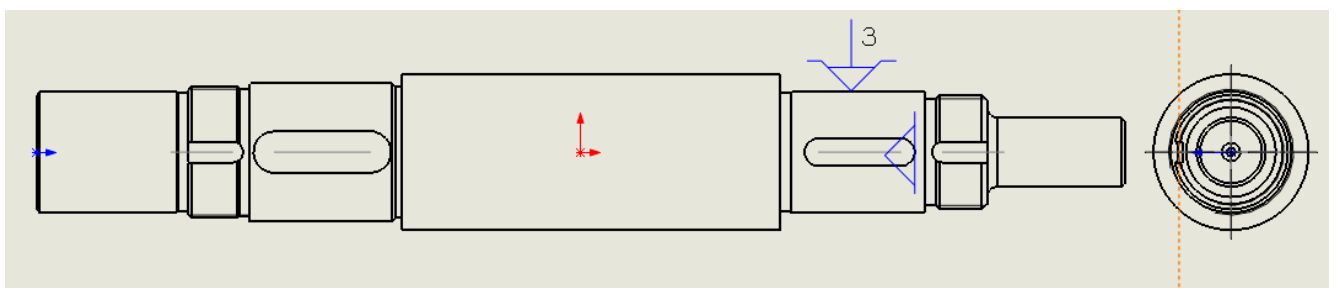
Теоретична схема базування обробки поверхонь 3 – 9.
